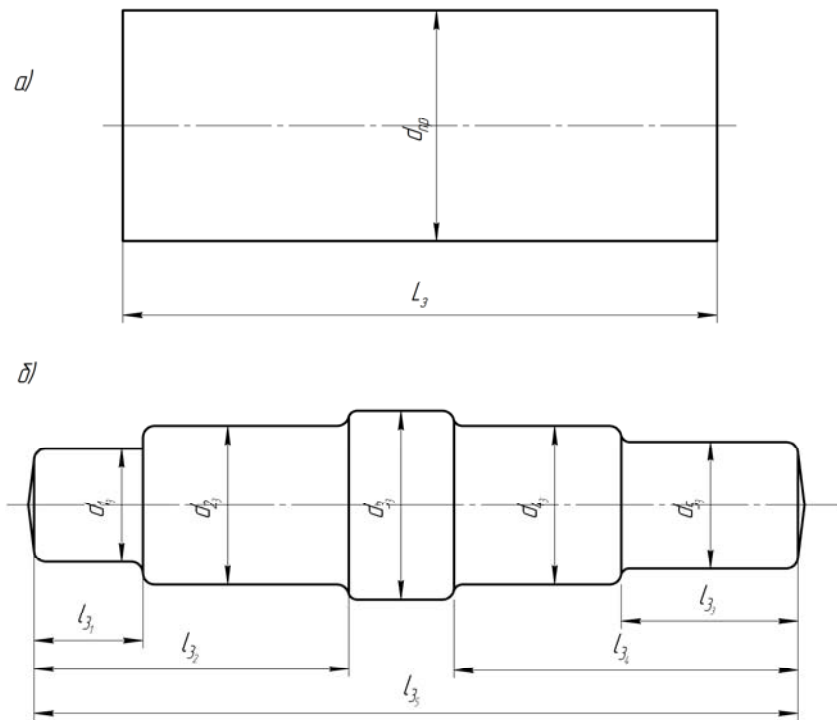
Чертеж заготовки (а – порезка из проката; б – штамповка на ГКМ)
